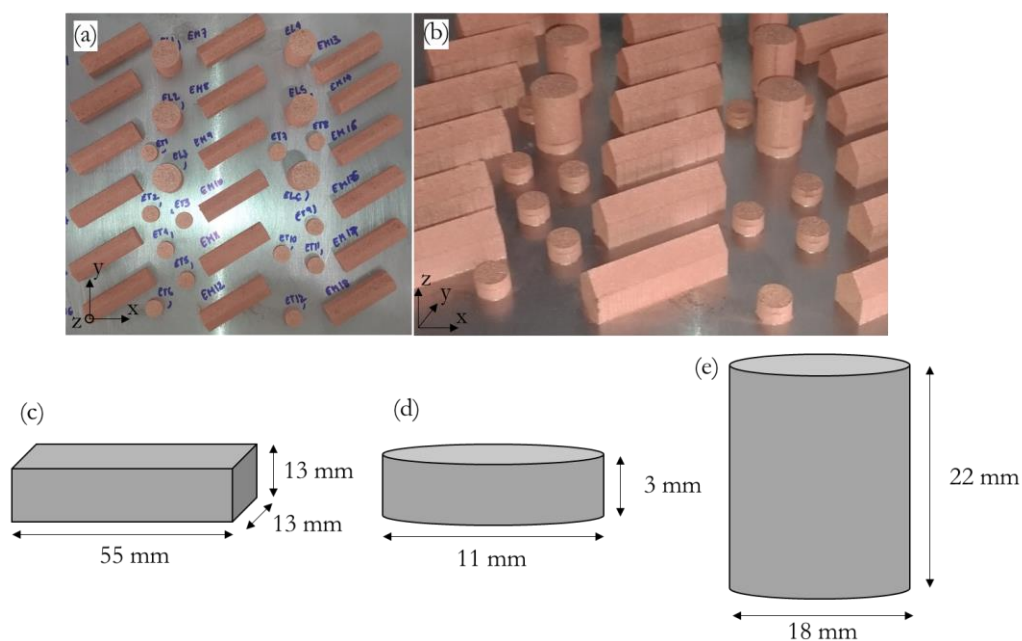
(a et b) Plateau FS271 des ébauches des éprouvettes et leurs dimensions : éprouvettes (c) mécaniques, (d) de diffusivité thermique et de capacité thermique et (e) électriques.
